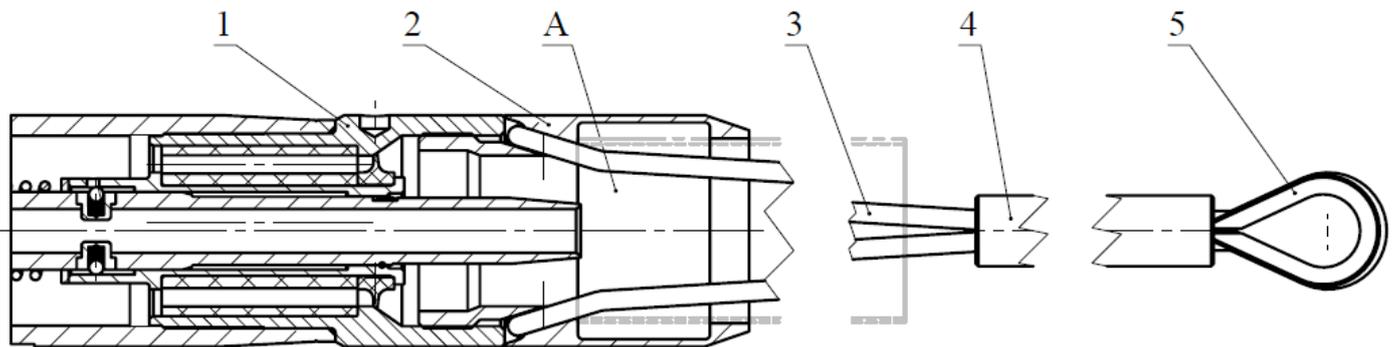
Схема сборки пробойника для протяжки труб (по заказу):
